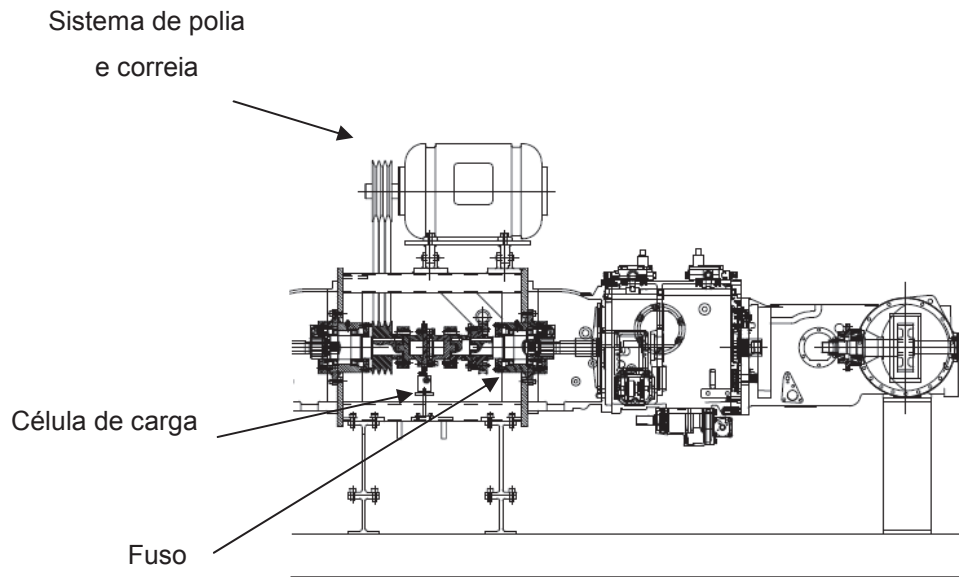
Bancada de teste, com um *Power Train* montado
